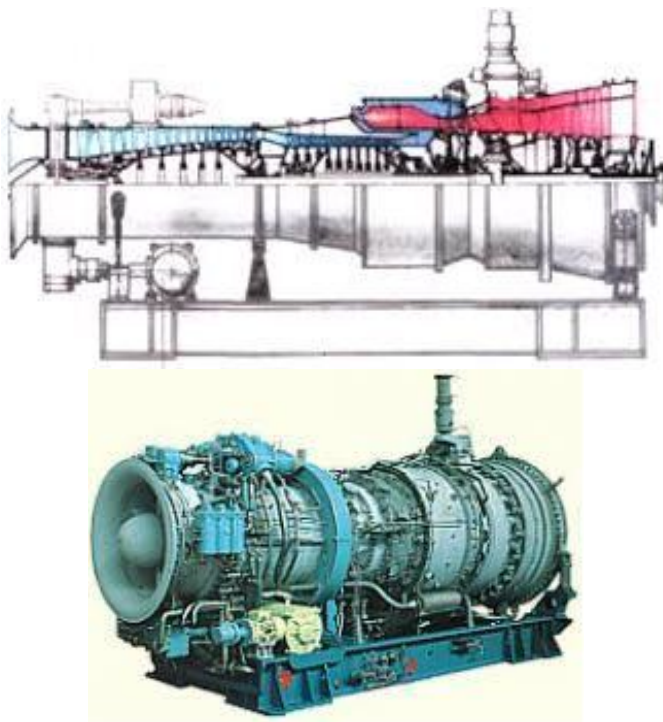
Газотурбинный двигатель с реверсивной газовой турбиной винта
